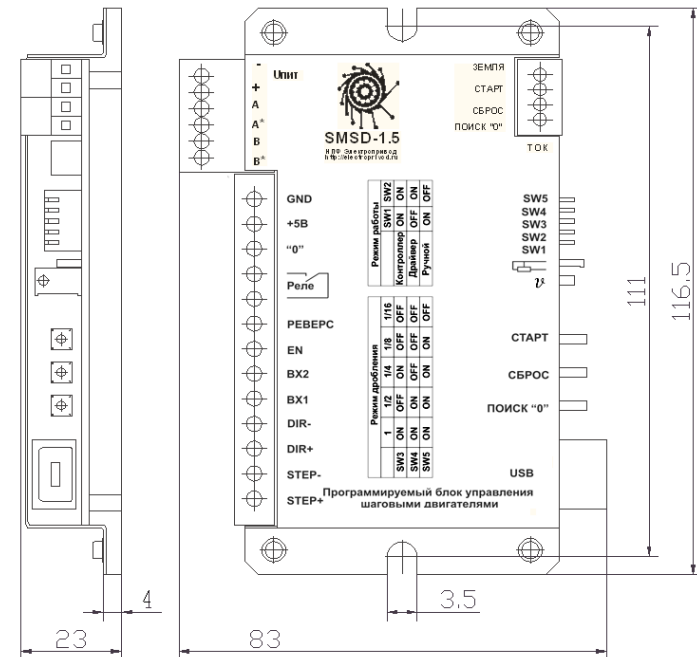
Габаритные размеры блока управления SMSD-1.5
